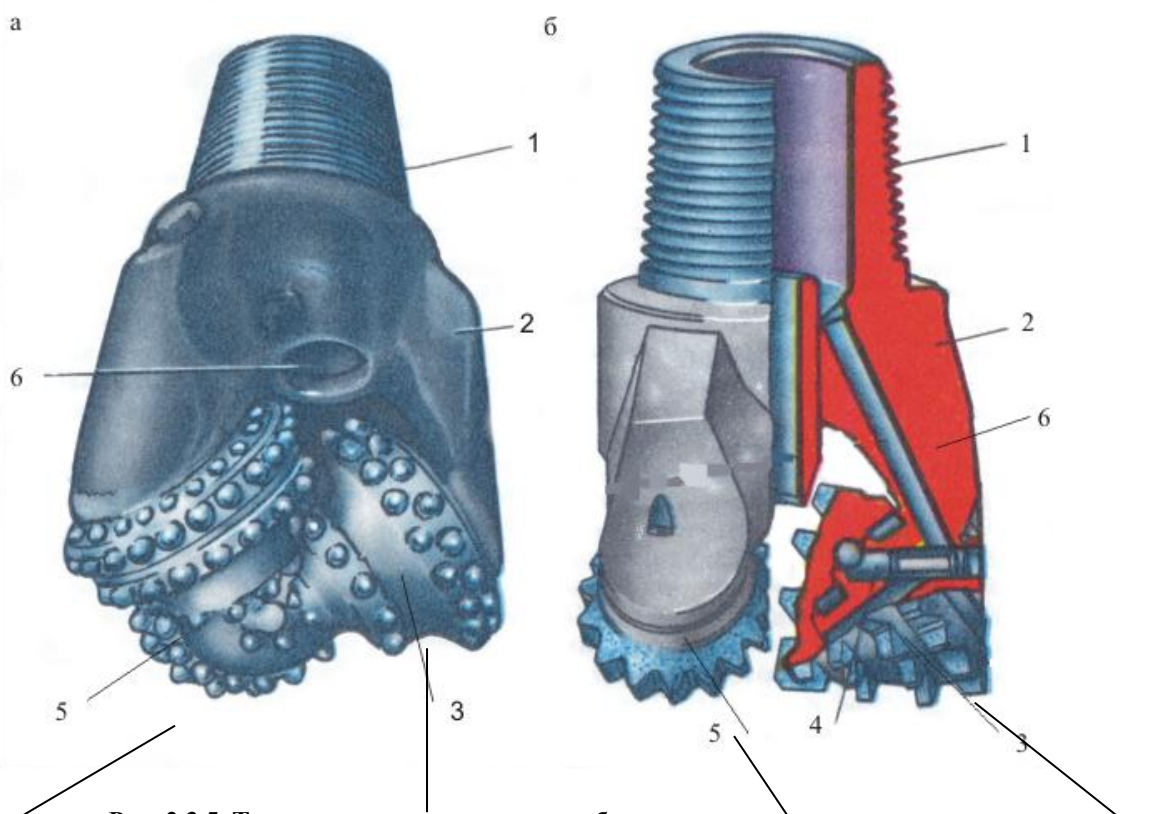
Трех шарошечное долото для бурения взрывных скважин с твердосплавными (а) и фрезерованными (б) зубками:
